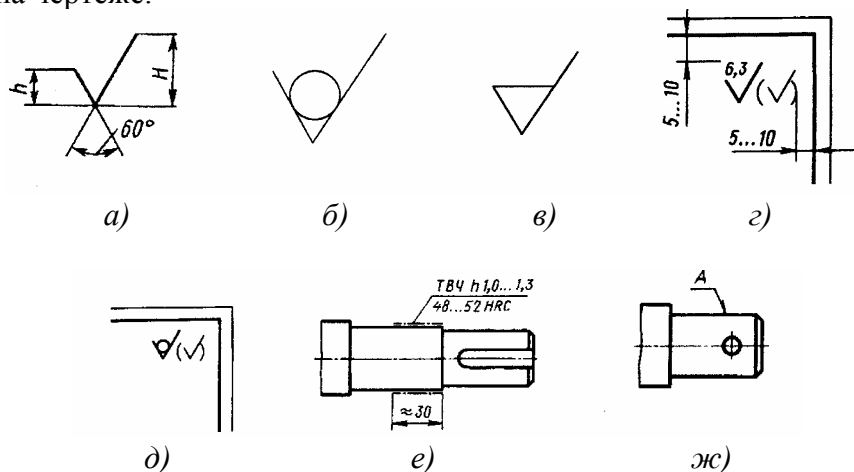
Знаки шероховатости и другие обозначения, указываемые на чертеже
